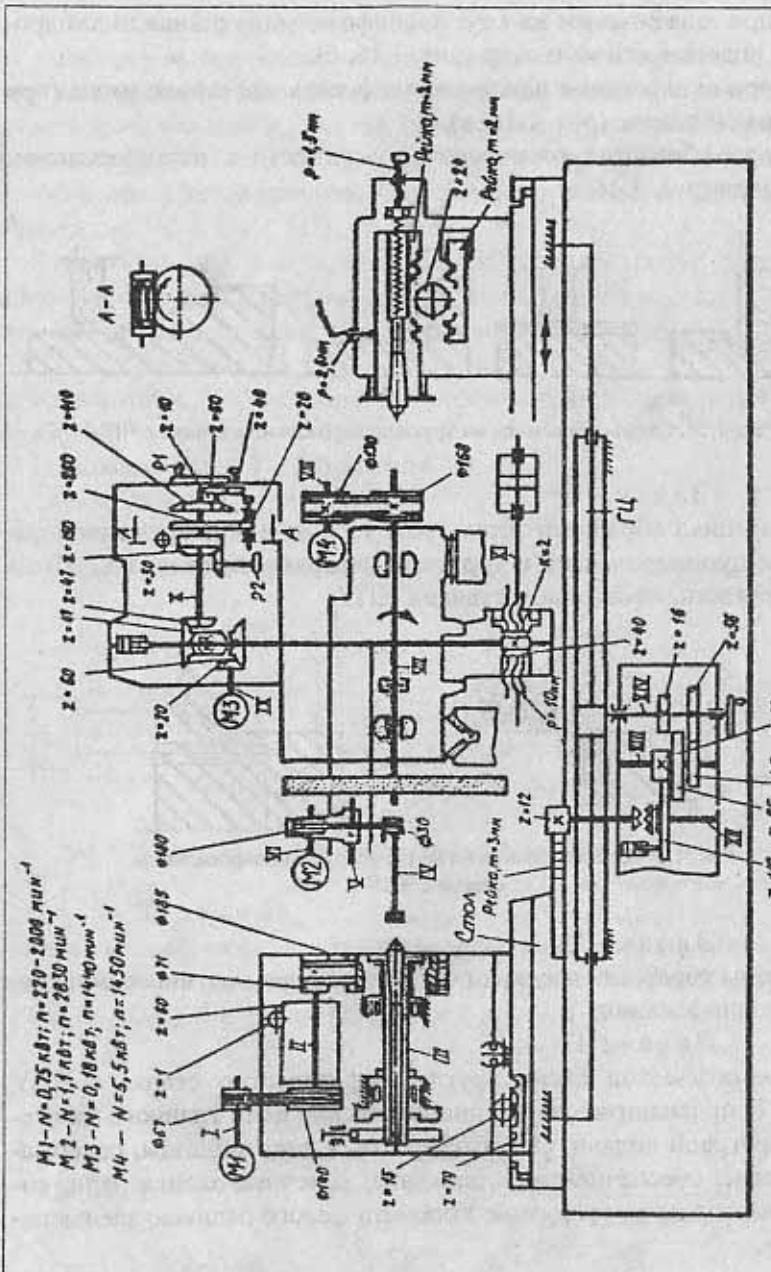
Кинематическая схема круглошлифовального станка мод. ЗУ131
